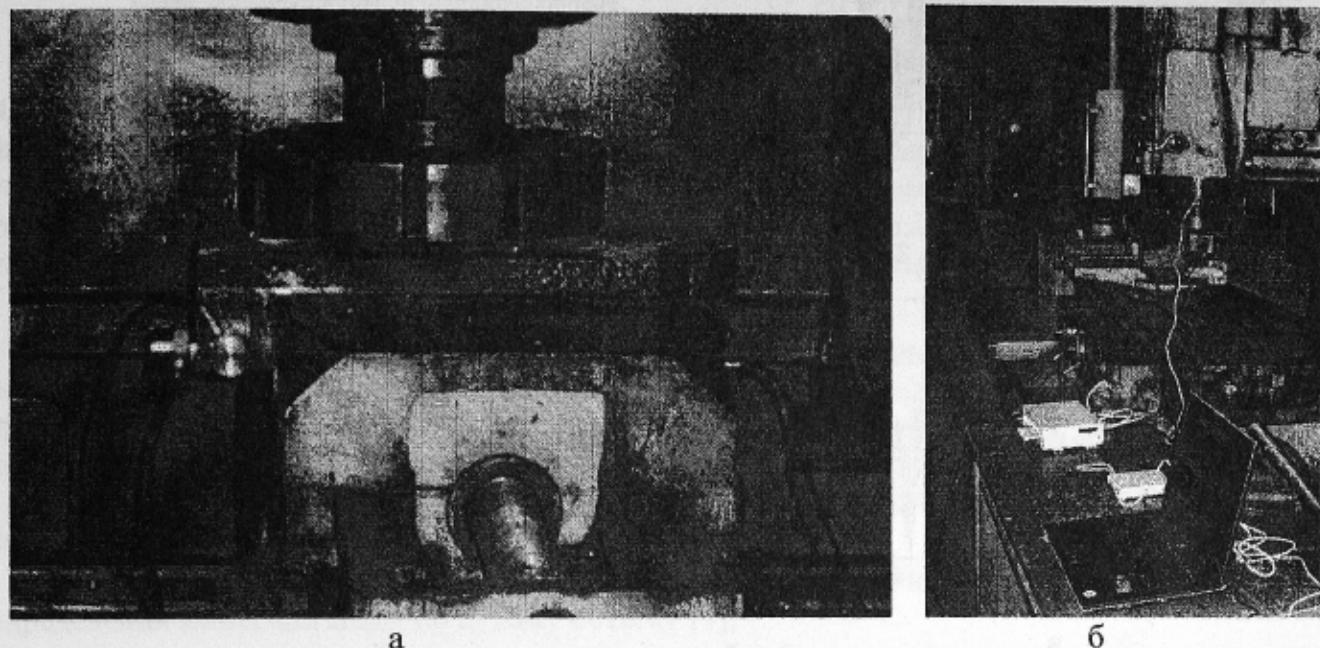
Измерительный стенд на фрезерном станке ЛГ 26: а-крепление датчиков виброускорений, б – общий вид
